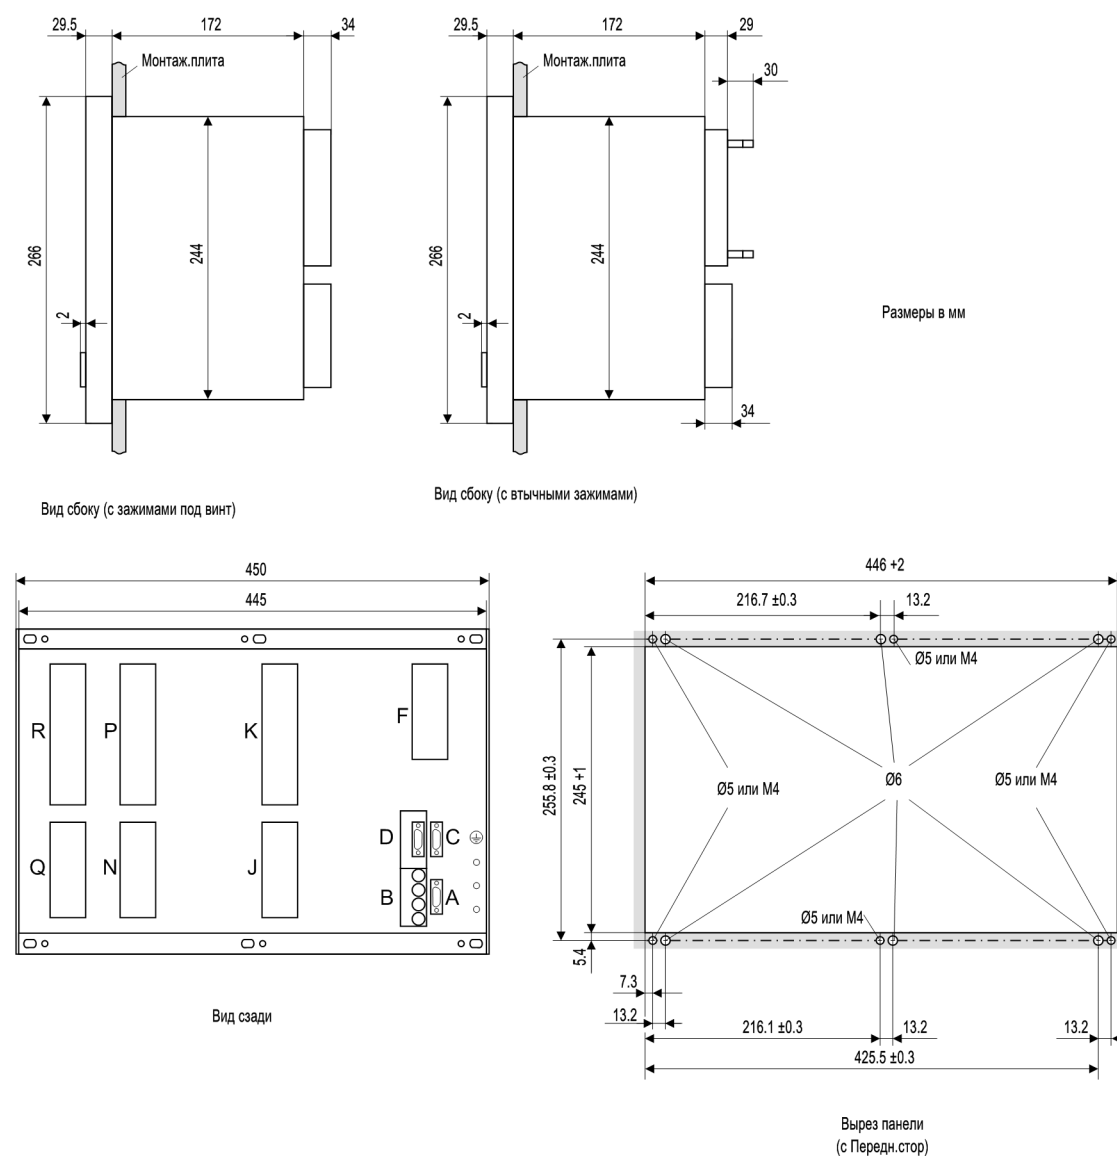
Размерные эскизы варианта устройства 7UM622 для встраиваемого монтажа устройства в шкаф / панель (размер корпуса 1/1)
